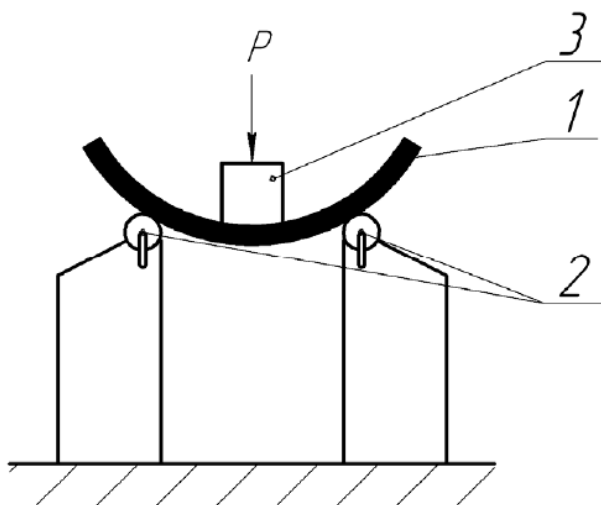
Проба на изгиб: 1 – образец; 2 – валки; 3 – пуансон
